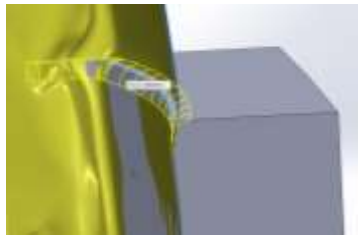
Pieza seccionada con plano a 55mm de la base.
